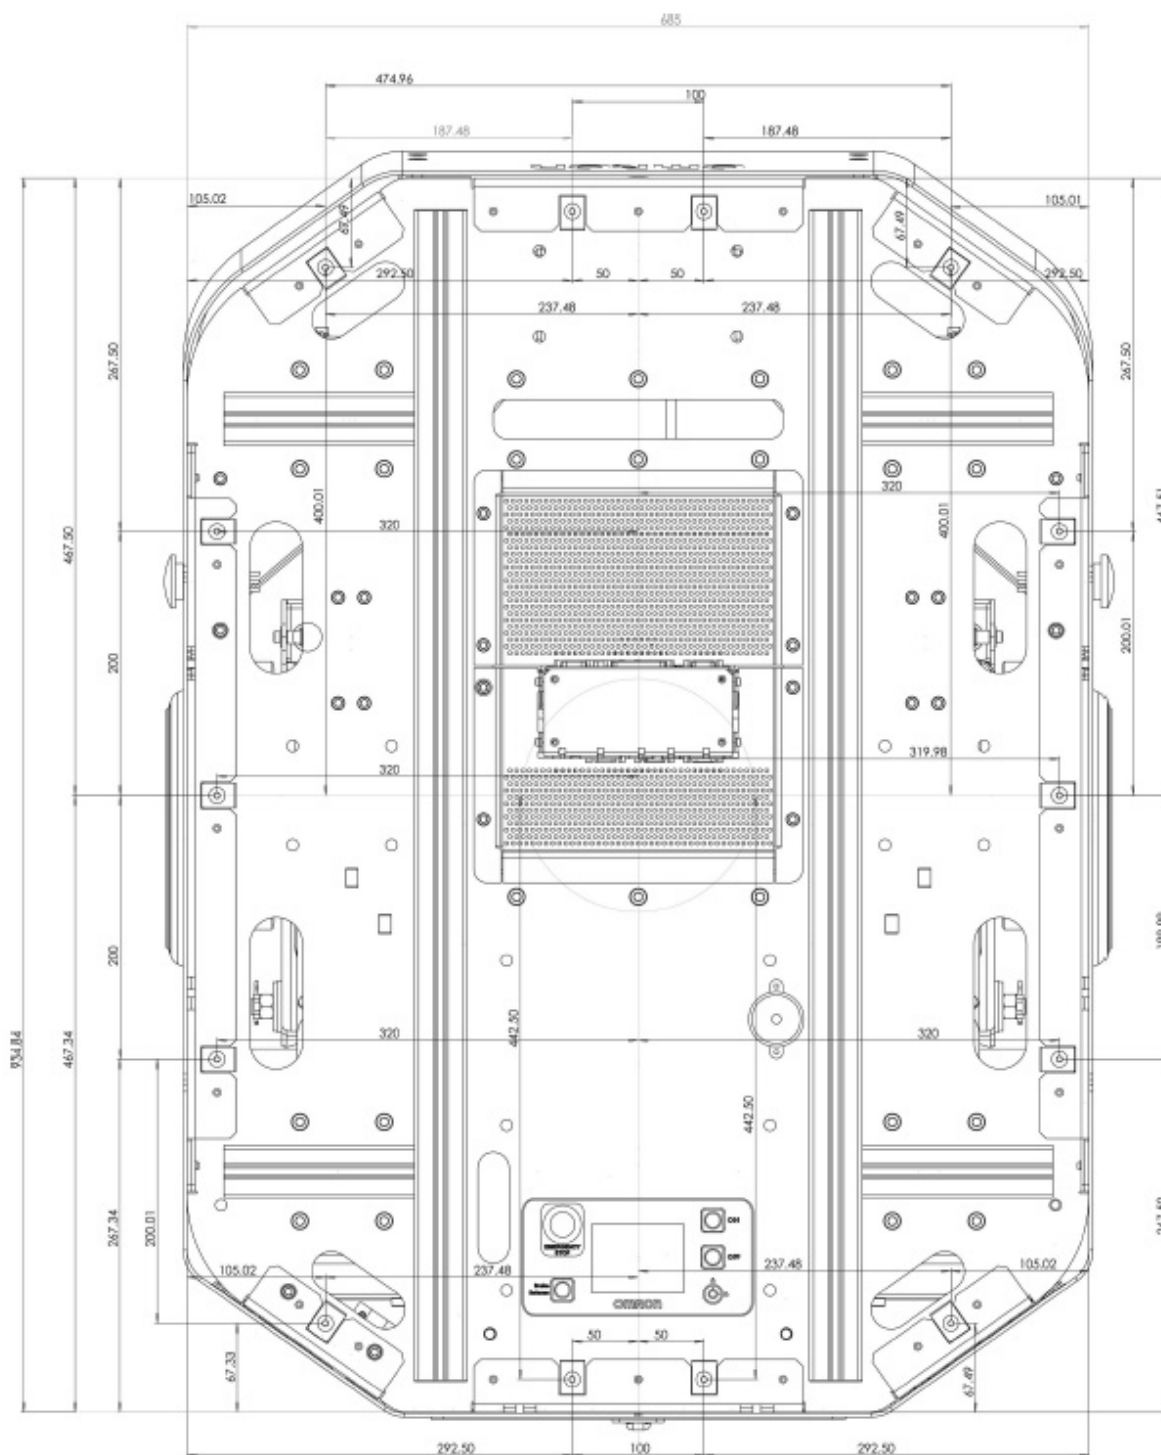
Placering av klämmuttrarna runt lastutrymmet
